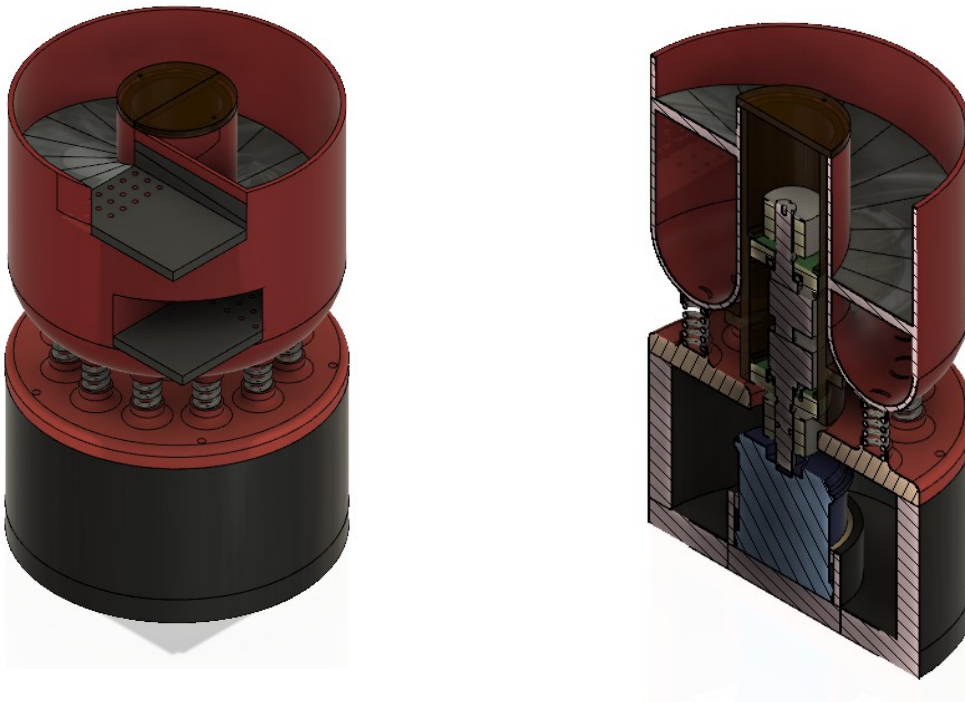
Acoplamiento del tambor de pulido y fin de montaje.
